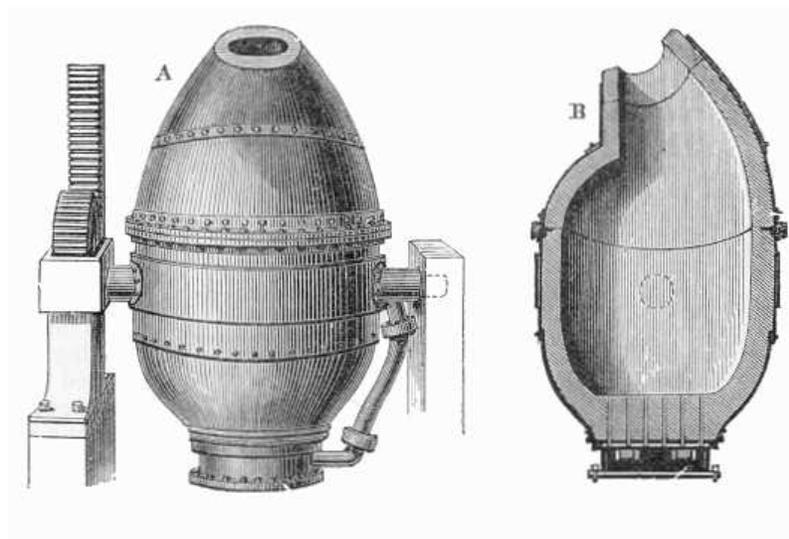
Antiguo Horno Bessemer para fabricar acero.
